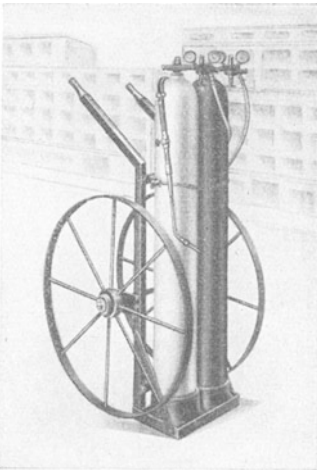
Fahrbare Flaschenazetylen-Schweißanlage.
